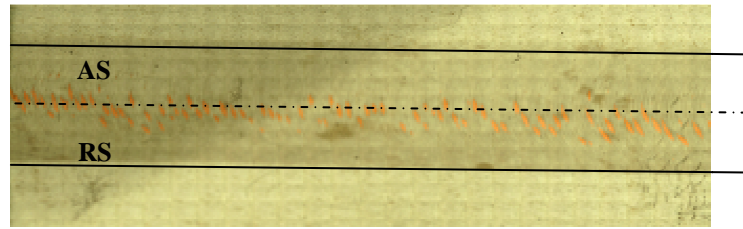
Cas de soudage 8, macrographie en pied de soudure.
